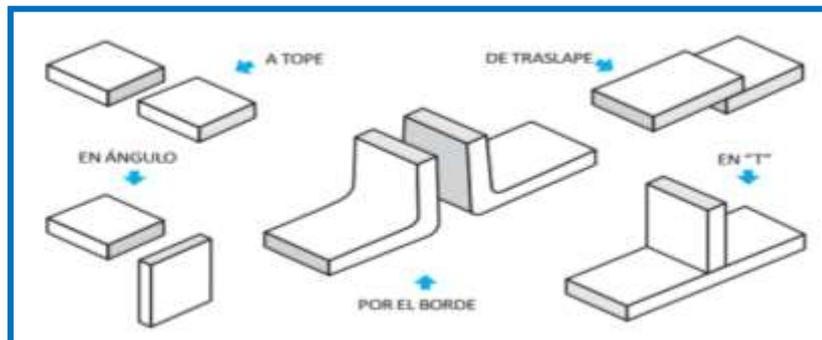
PREPARACIÓN DE JUNTAS PARA LA SOLDADURA
